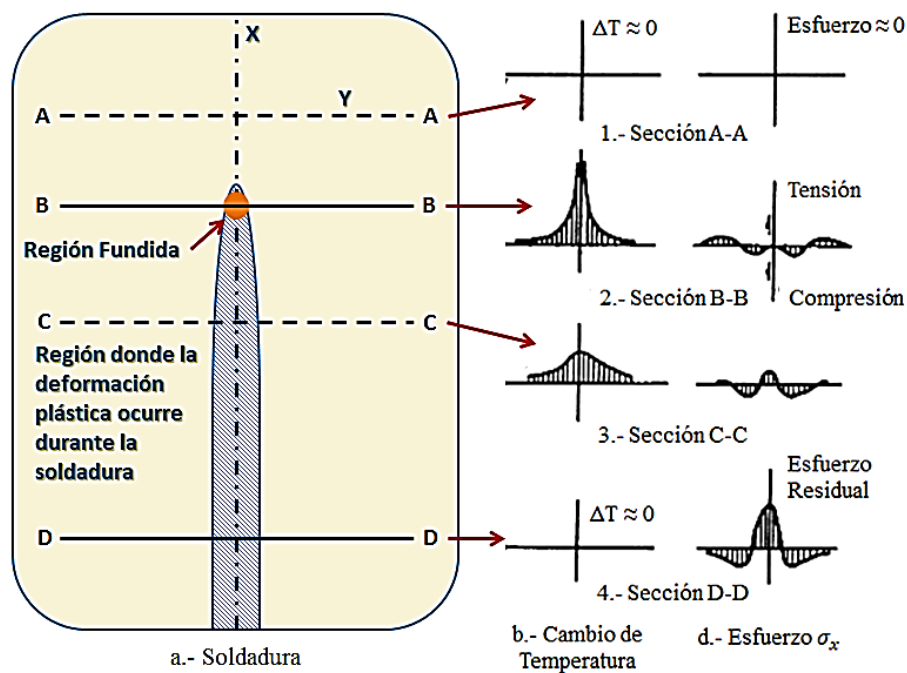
Cambio de temperatura y esfuerzo durante la soldadura^[34]
